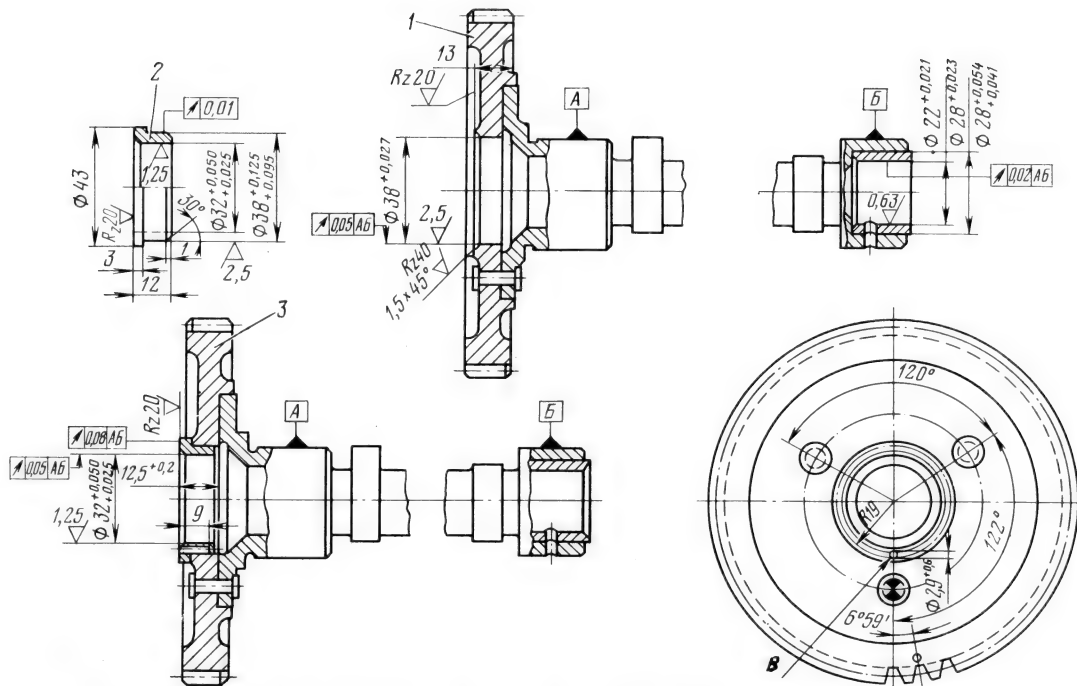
Расточка шестерни распределительного вала под ремонтную втулку:
